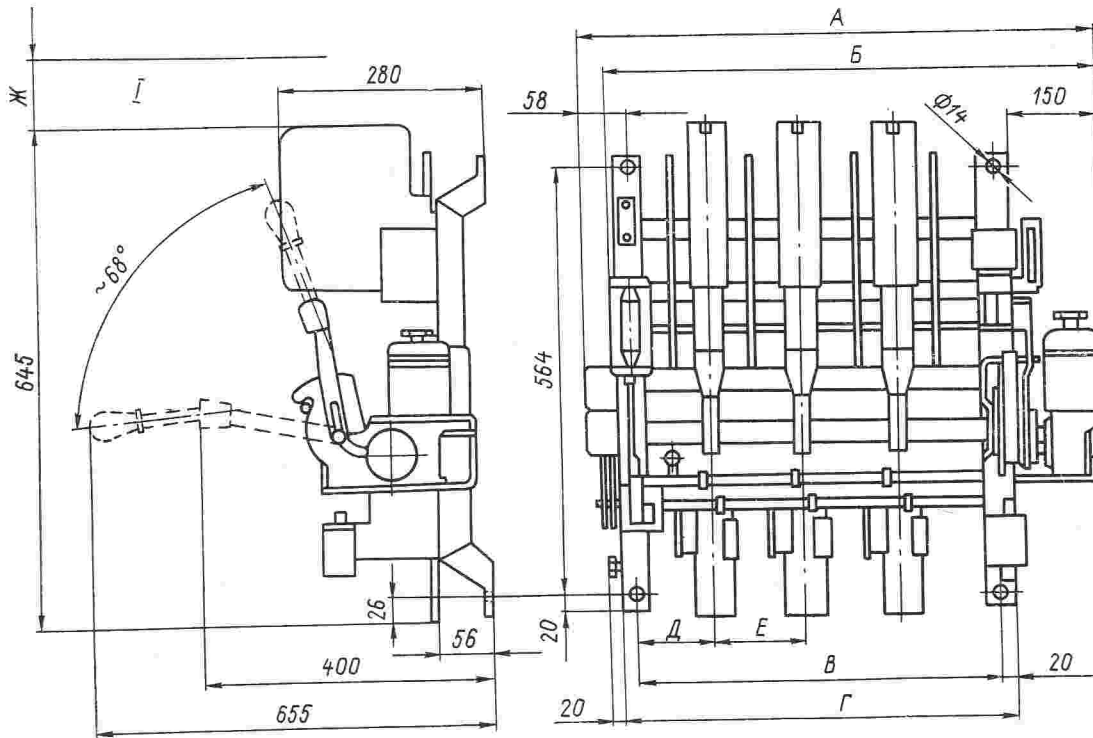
Габаритно-установочные размеры стационарных выключателей с электродвигательным приводом:
